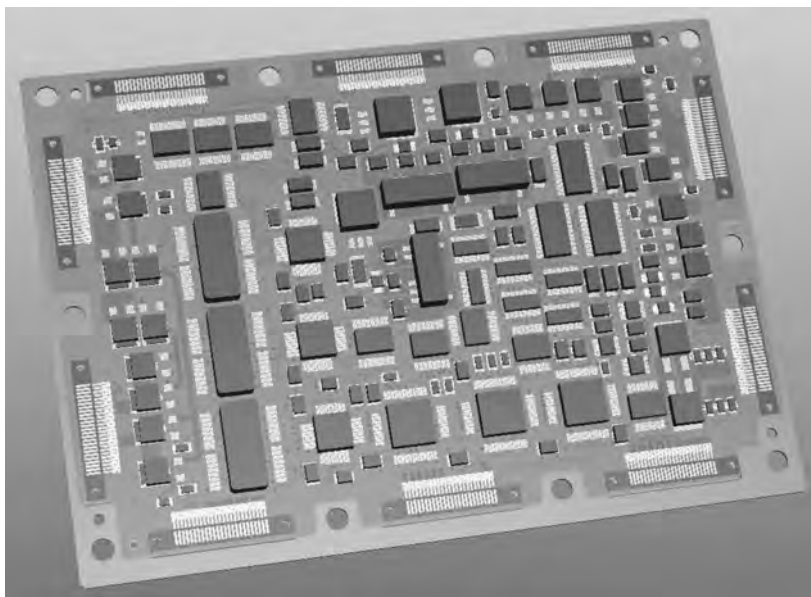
Образец устройства, выполненный при помощи Altium Designer
